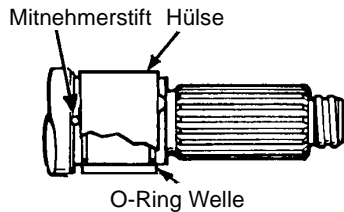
Entfernen Sie die Wellenschutzhülse
